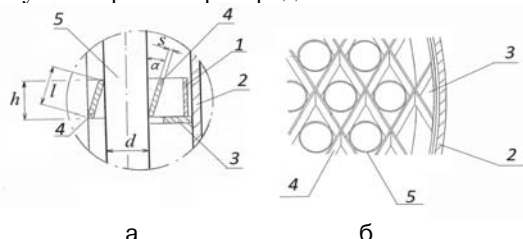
Опорная конструкция: а – установка перегородки внутри корпуса; б – расположение опорных полос в случае размещения труб по вершинам треугольника; 1 – кольцо; 2 – корпус; 3 – опорное кольцо для крепления к корпусу; 4 – наклонные полосы; 5 – труба
